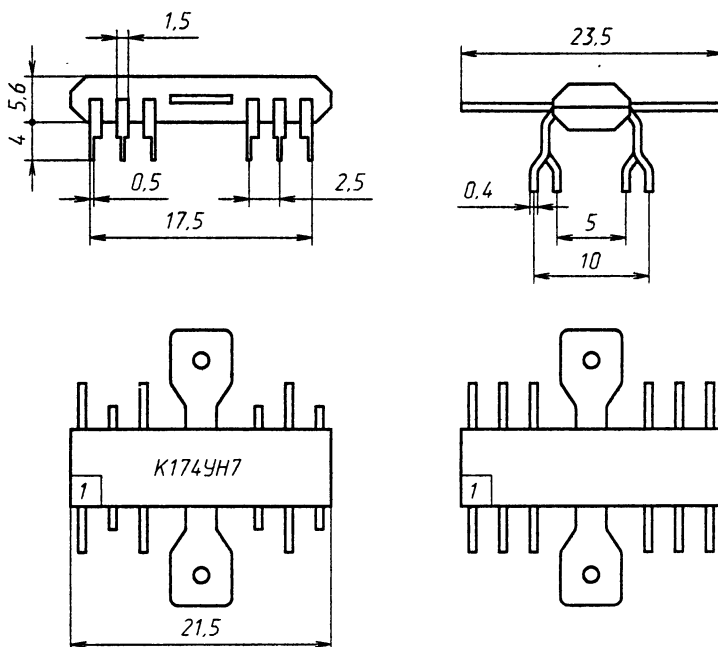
Внешний вид и габаритные размеры микросхемы К174УН7
